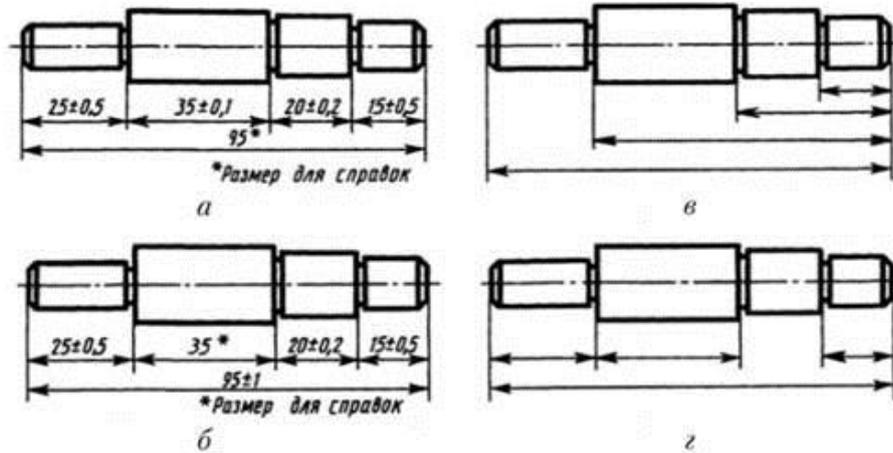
Способы нанесения размеров длины на чертеже вала:
